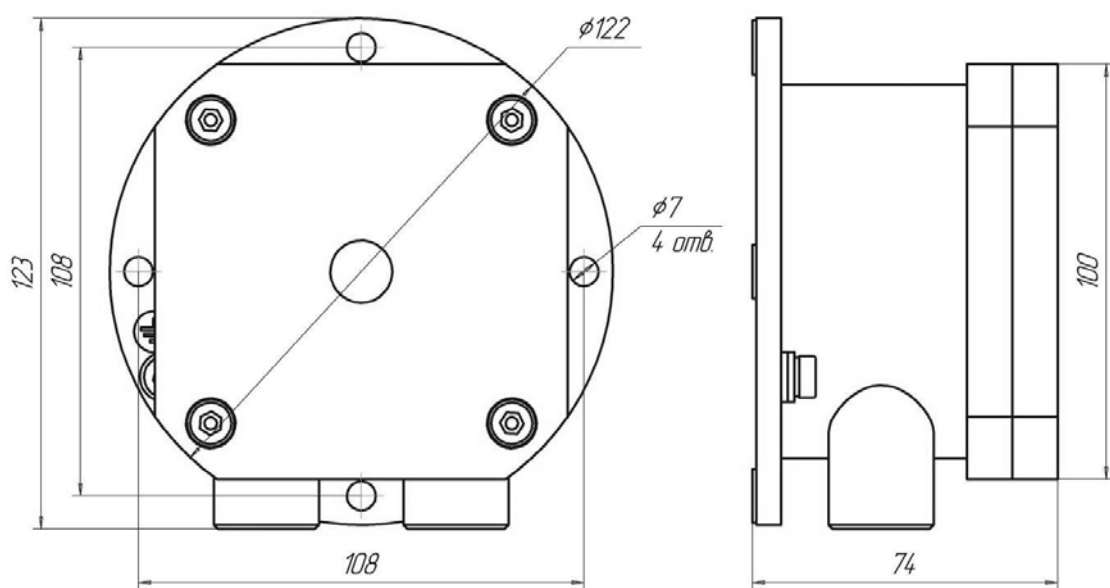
Оповещатель пожарный взрывозащищенный звуковой
